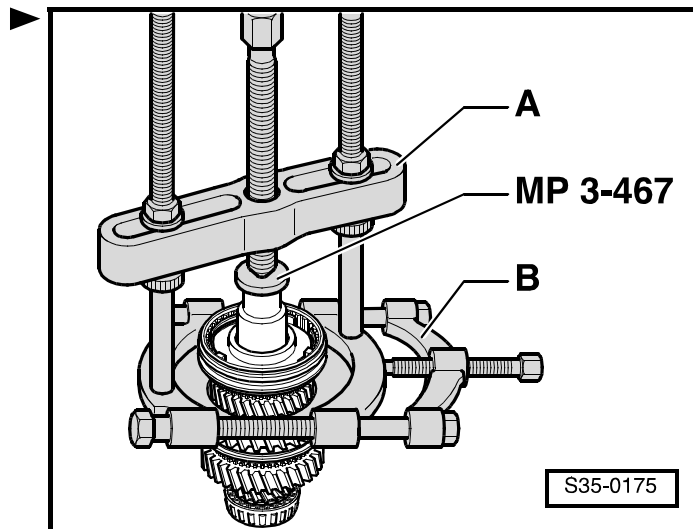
Выпрессовывание скользящей муфты и каретки синхронизатора 1-ой и 2-ой передач
